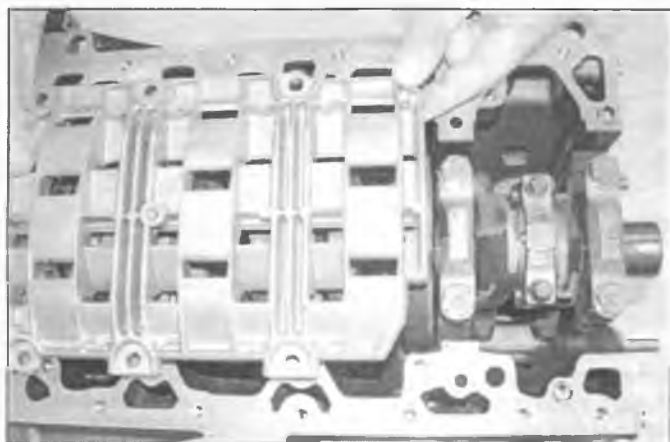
Выверните шесть болтов и снимите усиленную пластину с блока цилиндров
